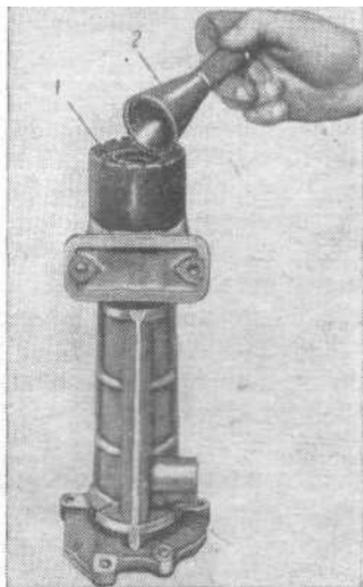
Запрессовка сальников в горловину удлинителя коробки передач при помощи оправки
